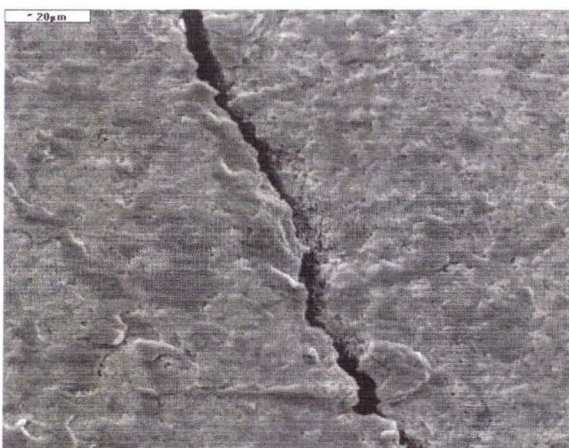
Observation d'une fissure sur l'outil instrumenté.
